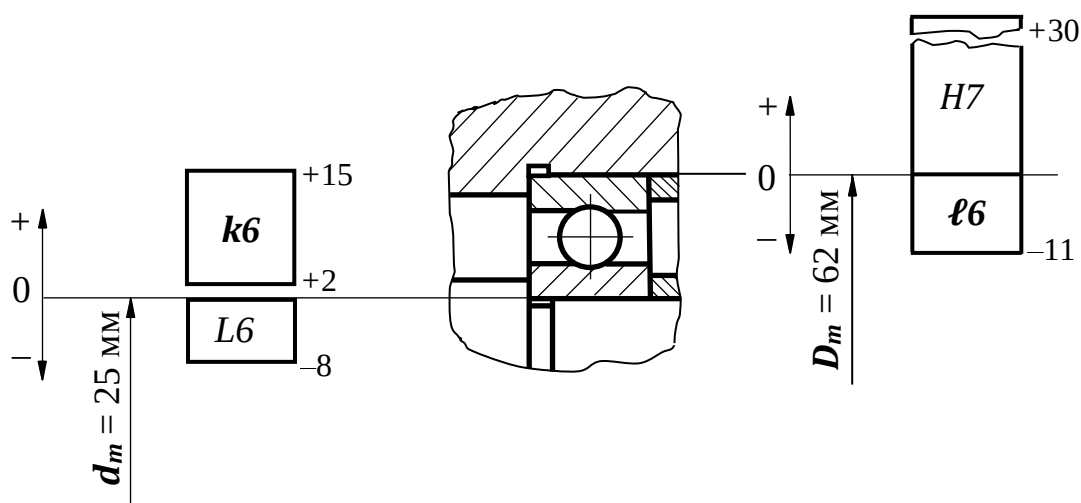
Схемы полей допусков посадок колец подшипника 6-305 в корпус и на вал
